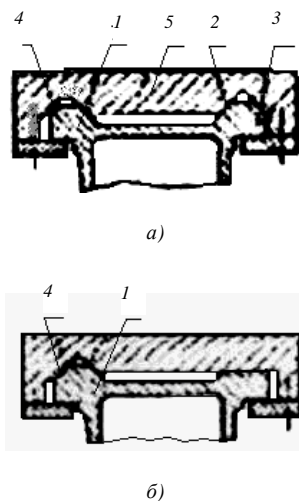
Варианты конструкции направляющей токарных станков
